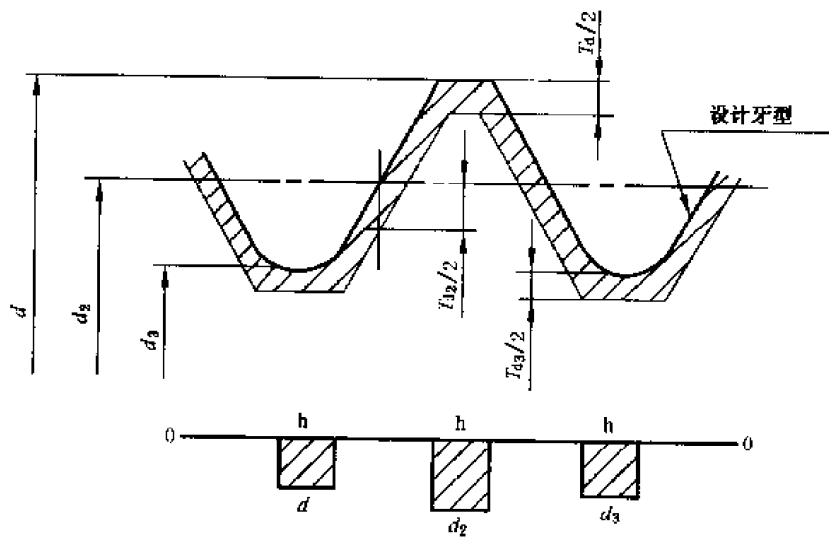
外螺纹公差带(5h3 或 5h5)的位置
